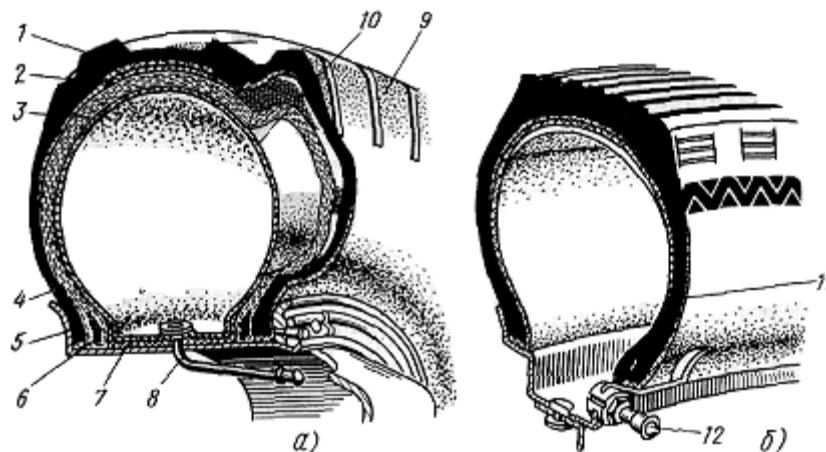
Пневматическая шина: а - камерная; б - бескамерная; 1 - протектор; 2 - брекер; 3 - каркас; 4 - боковина; 5 - борт; 6 - сердечник; 7 - ободная лента; 9 - покрывка; 10 - камера
